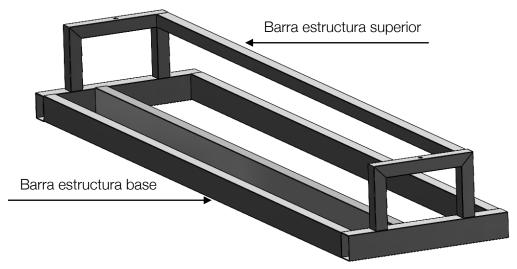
Vista isométrica de la estructura soldada. Fuente: elaboración propia.
